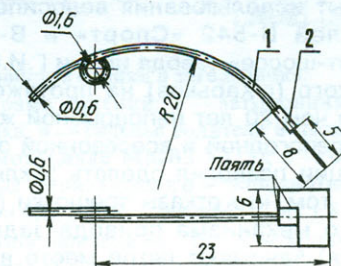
Сборная пружина: 1 — дуга; 2 — лопатка.
